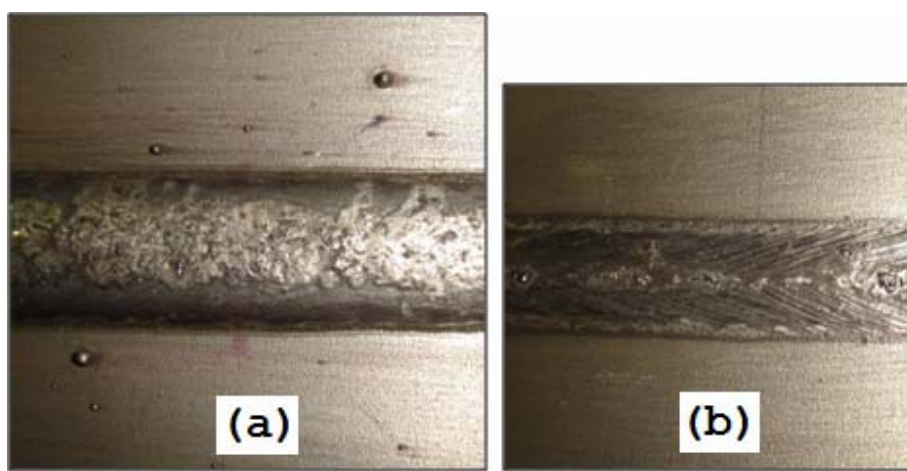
Aspecto dos cordões de solda obtidos com (a) 1,8 kJ/mm e (b) 1,1 kJ/mm.
